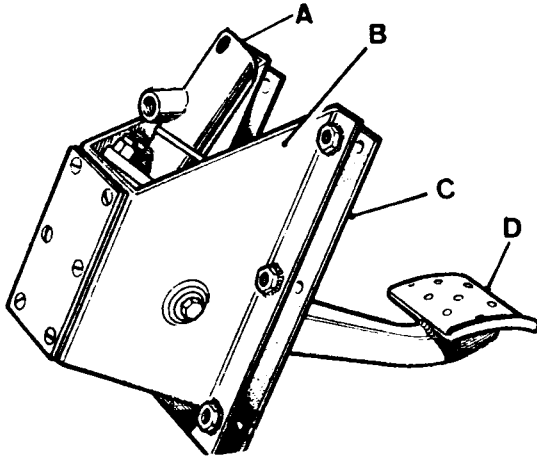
Conjunto del soporte, pedal y cilindro principal.
